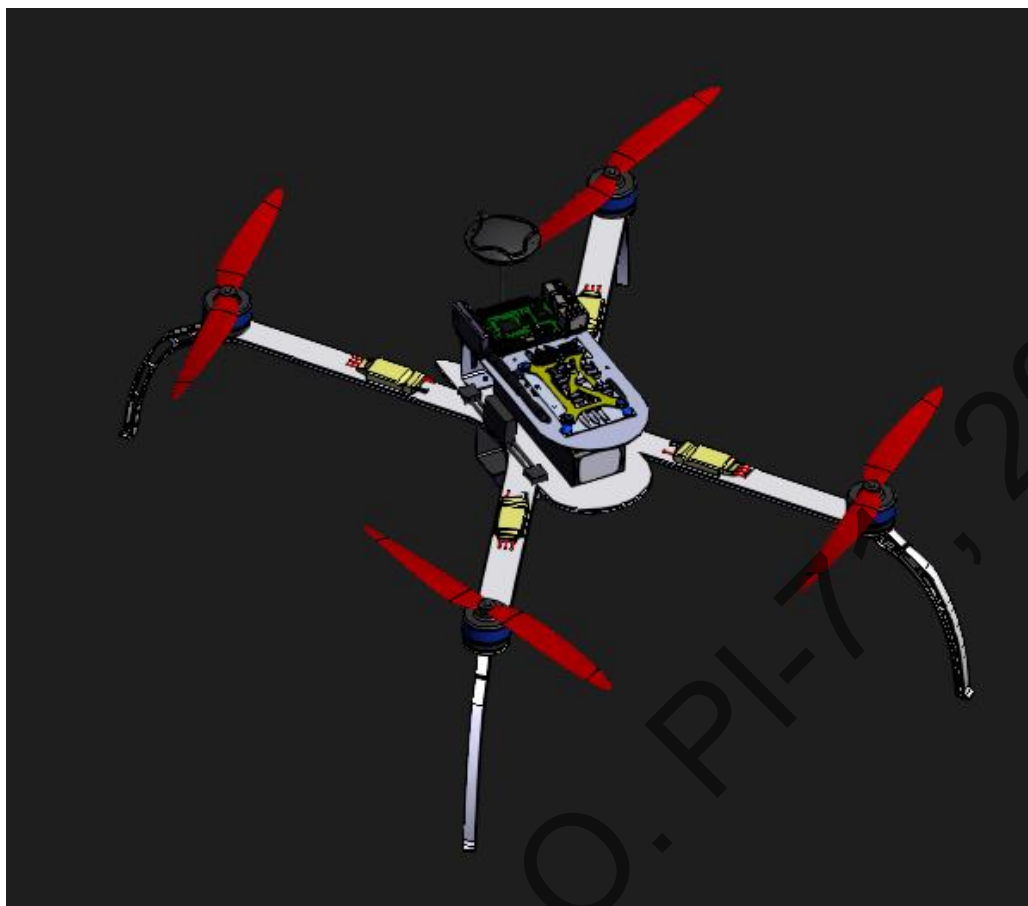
Корпус квадрокоптера в середовищі SolidWorks
